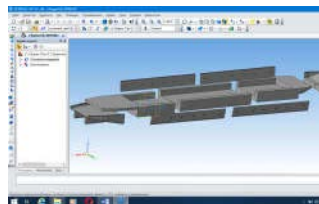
Процесс сборки основных элементов, носовой и кормовой частей 3D-модели НС
